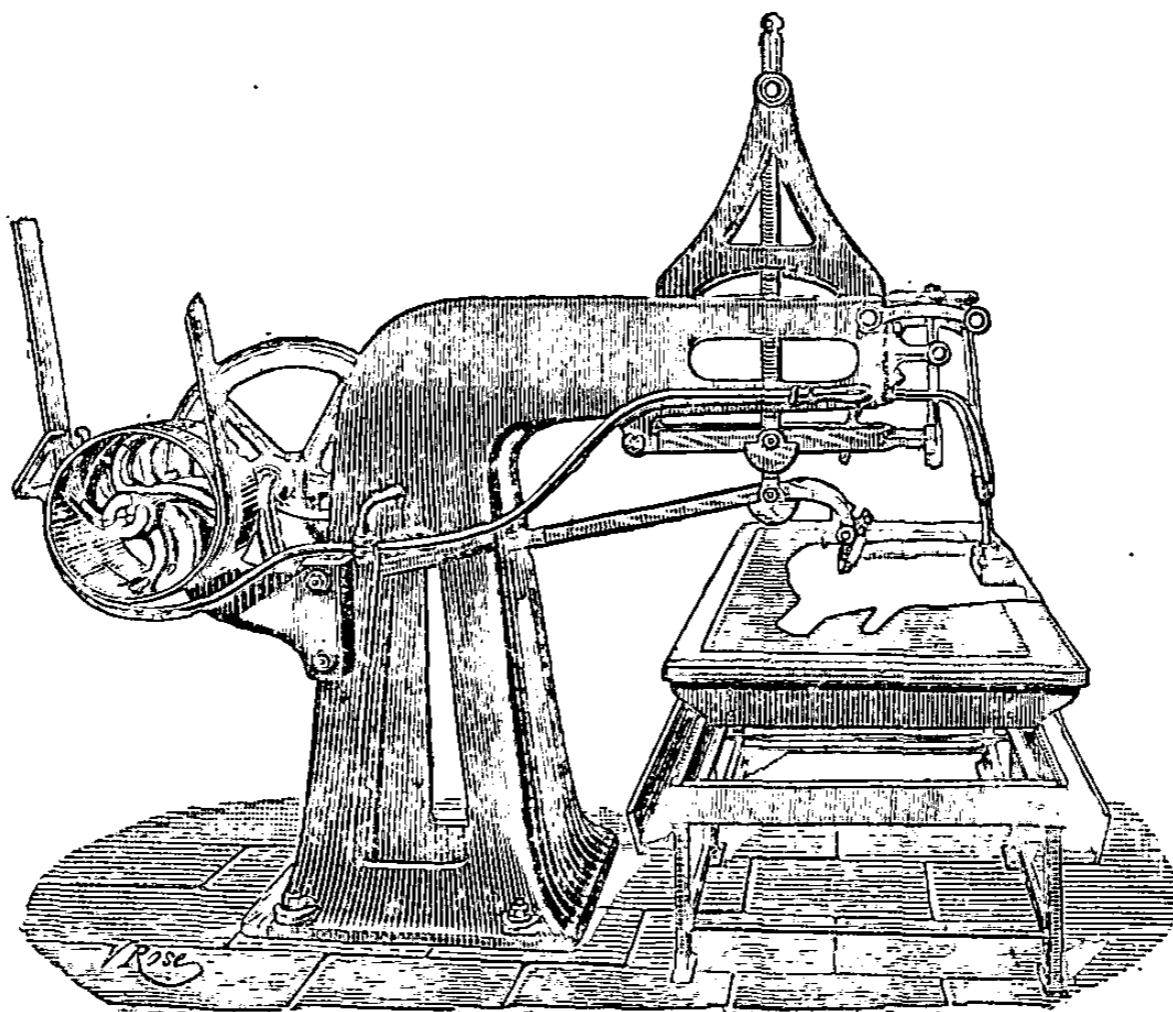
Machine Allard à travailler les cuirs de corroierie.
